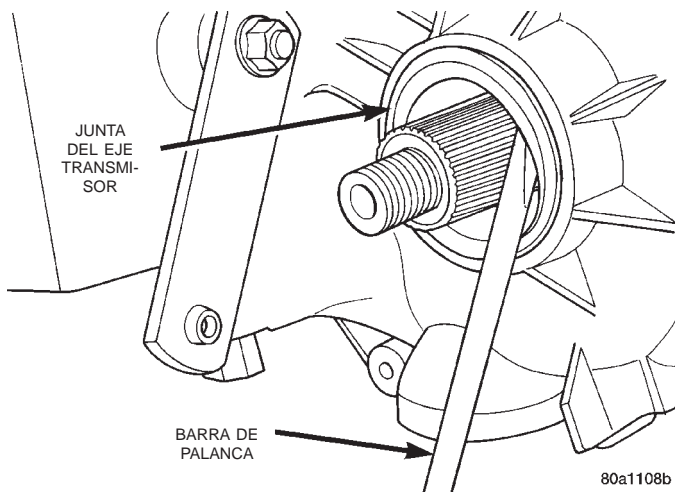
Desmontaje de la junta del eje transmisor delantero
